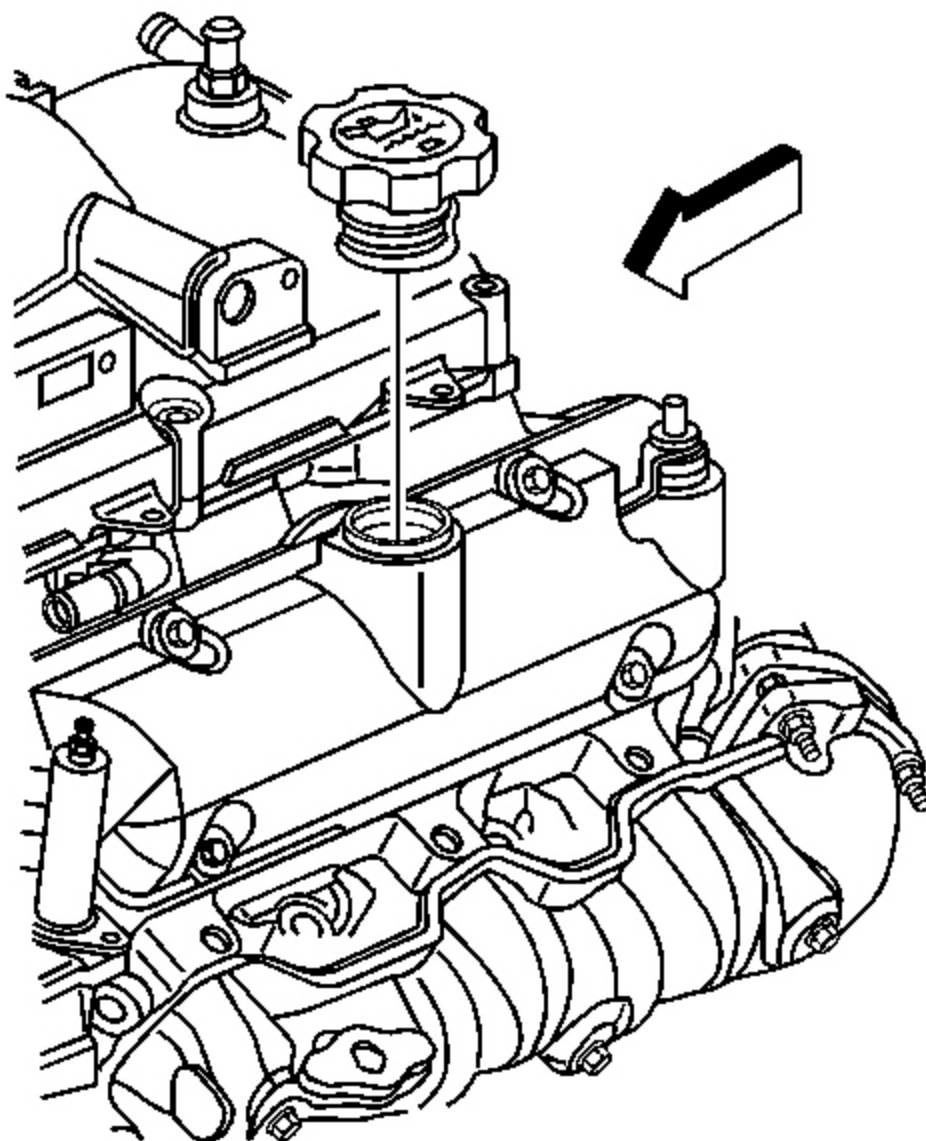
Vista de la válvula cubierta de balancines - Cortesía de General Motors Corp Izquierda.
